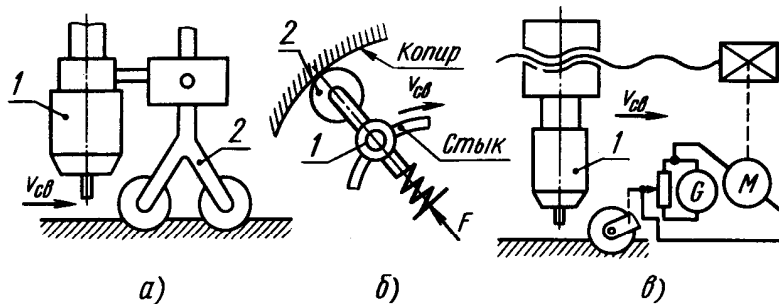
Схемы соединений копирующего ролика со сварочной горелкой: а, б- жесткие; в- гибкое
